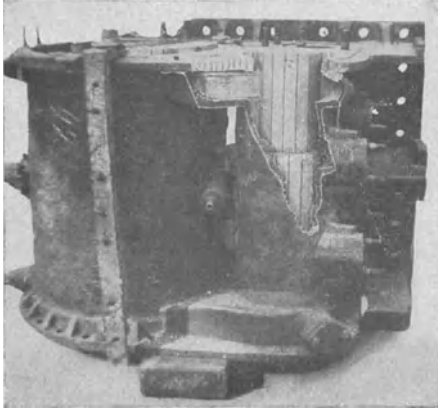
Lokomotivzylinder vor der Schweißung.
